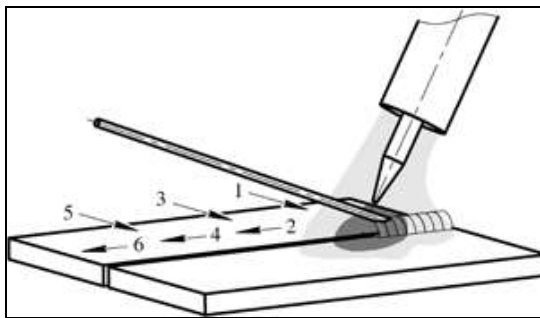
Пример манипуляции присадочной проволокой при TIG сварке
